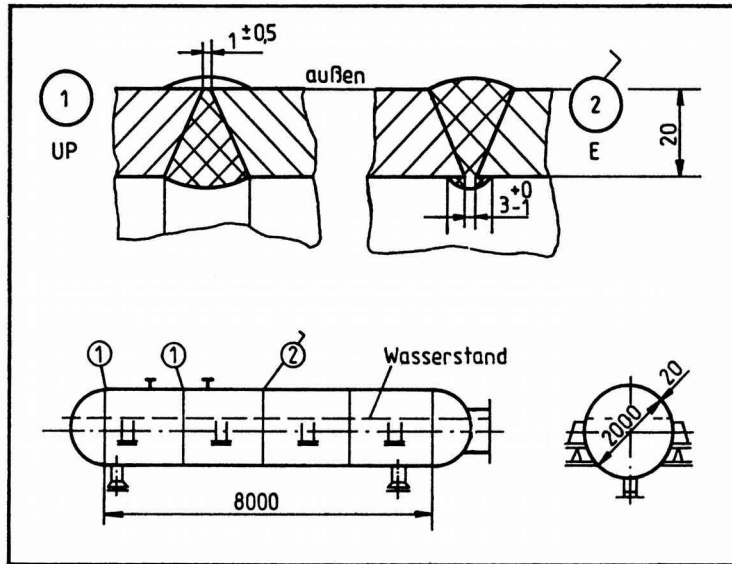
Heißwassererzeuger (schemat.) mit Hauptabmessungen und Schweißnahtangaben, Werkstoff 19Mn5
